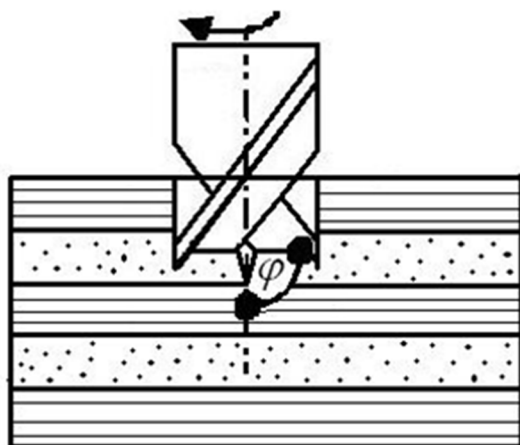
Схема сверления фанеры спиральным сверлом с центром и подрезателями
